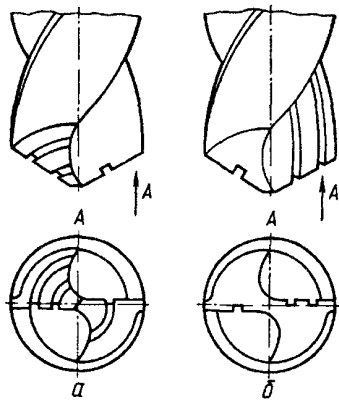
Стружколаміні канавки свердла на поверхнях: а - задній; б - передній
